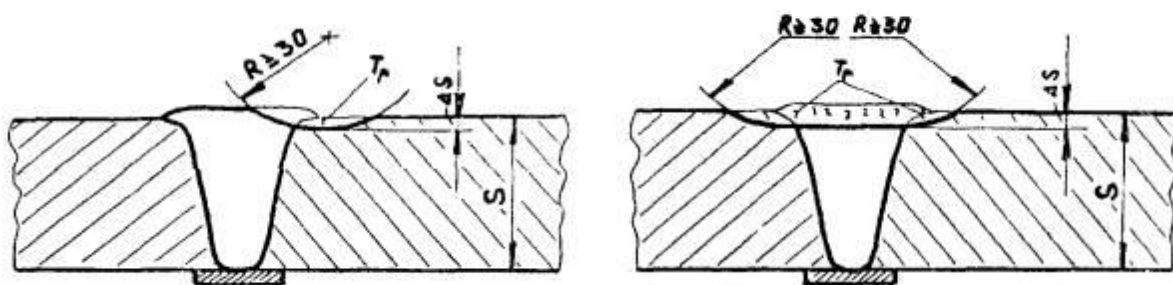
Схема исправления дефекта выборкой без подварки
